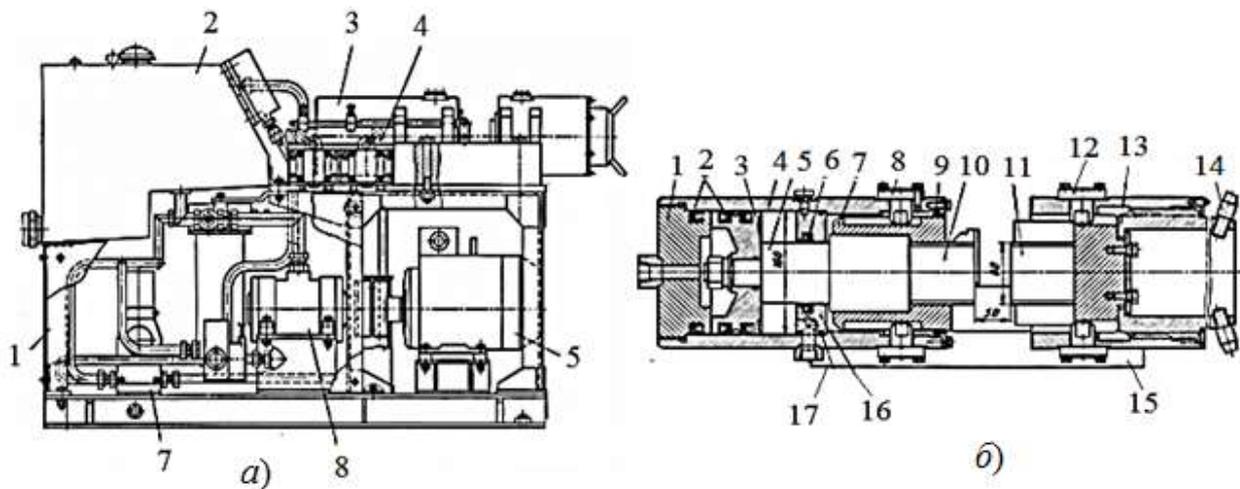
Станок СМЖ-133А для резки арматурных стержней: *а* – конструктивная схема; *б* – механизм реза.
